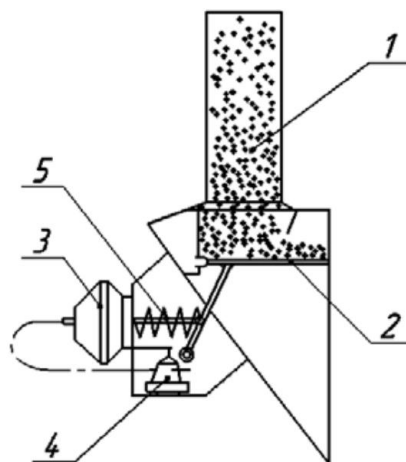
Шибєрний дозатор доїльної установки УДА - 16: 1 - приймальний бункер; 2 - шибєр (заслінка); 3 - мембрана; 4 - пульсатор; 5 - поворотна пружина
